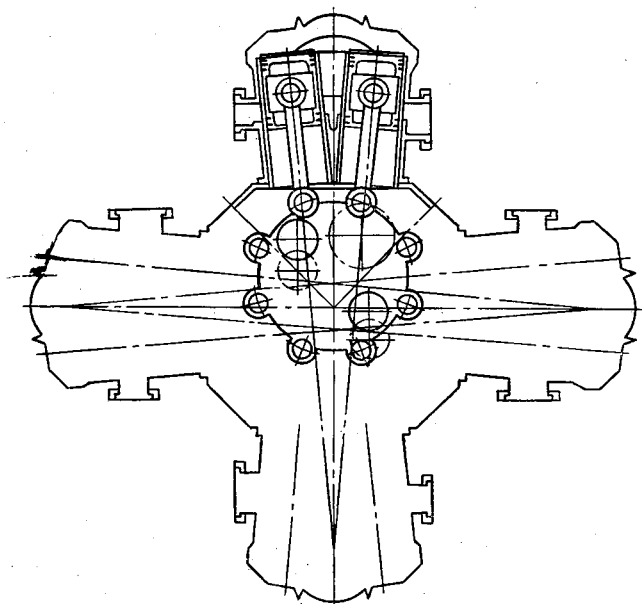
Кинематическая схема двигателя Дина-Стар с цилиндрами, расположенными под углом
